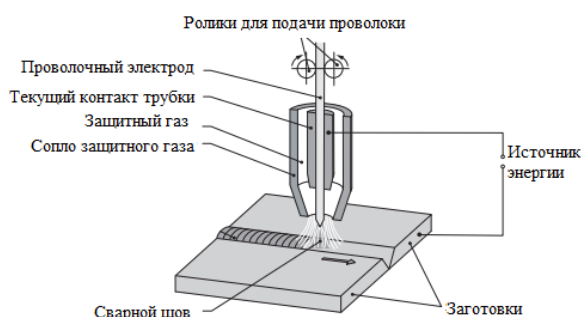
Принцип работы сварки в защитных газах
